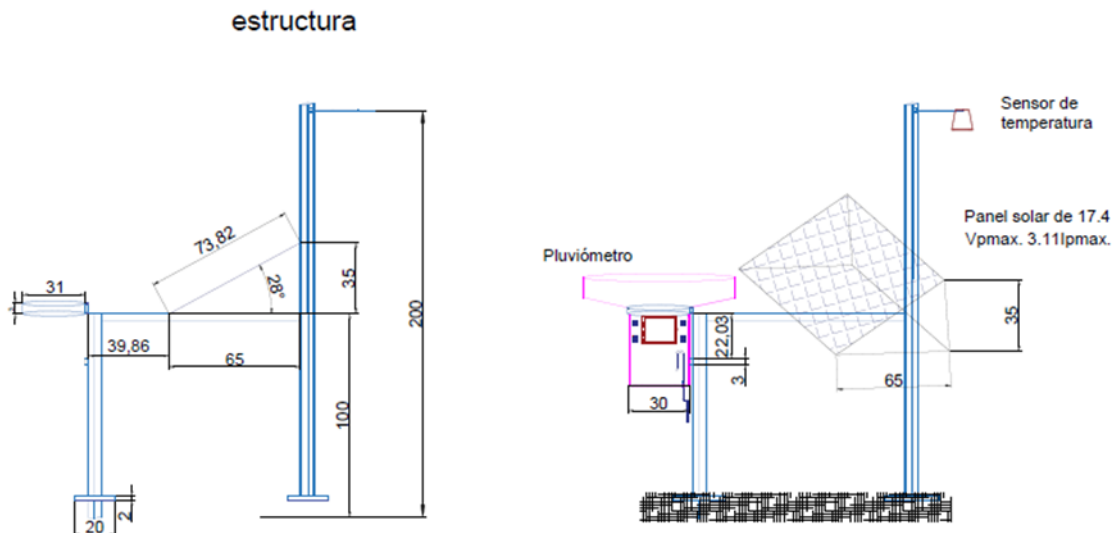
Plano de diseño de estructura de acero para montar dispositivo termopluviométrico.
